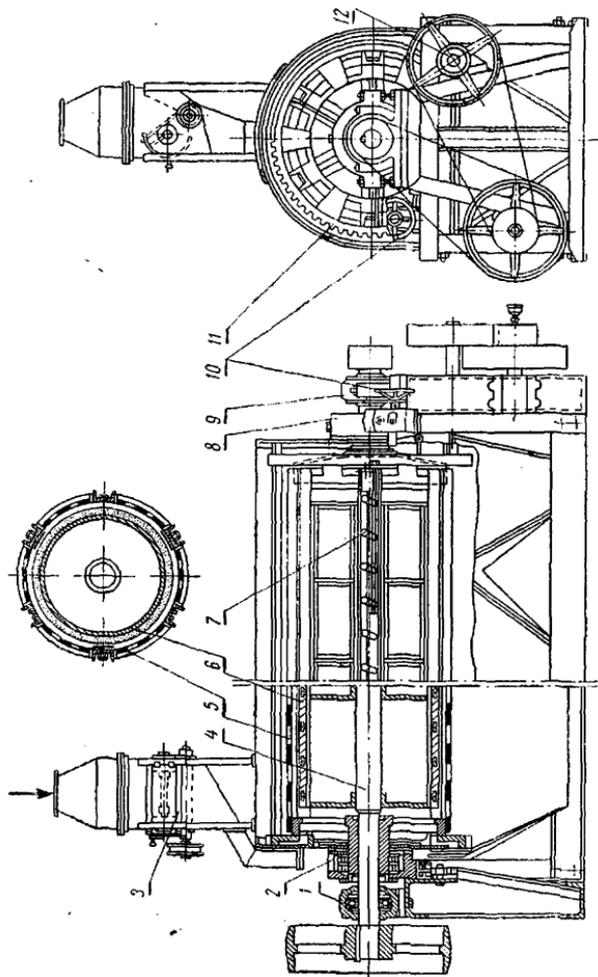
Шелушительная машина с абразивным барзбаном конструкции
